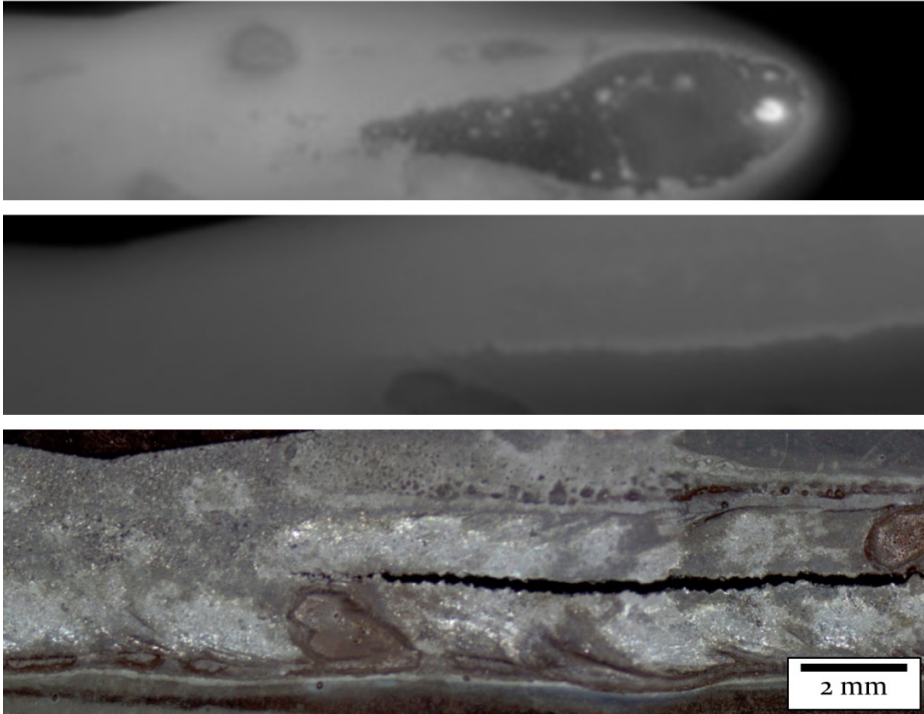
Oben: Einzelbild einer exemplarischen Schmelzbadgeometrie aus einer Thermografieaufnahme, Mitte: Einzelbild des im Schweißprozess entstandenen Nahtmittenrisses, Unten: Aufsicht der Schweißnaht mit Nahtmittenriss; $P = 1,00 \text{ kW}$; $v_L = 10 \text{ mm/s}$; $E = 100 \text{ J/mm}$; $d_F = 170 \text{ }\mu\text{m}$
